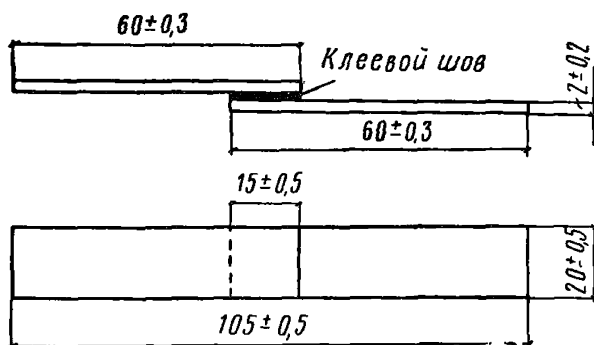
Стандартный образец для испытания клеевых соединений на сдвиг при растяжении
